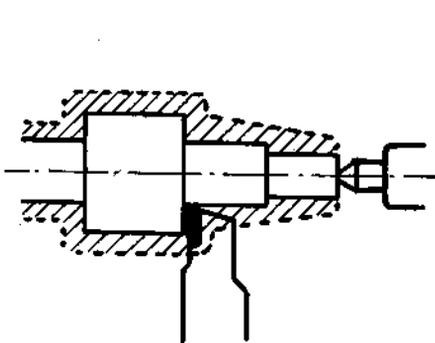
Ejemplo de copiado de una pieza estampada con sobre-espesores producidos por la conicidad de la estampa. La profundidad de corte es superior a la longitud de la pastilla de carburo de la herramienta.
